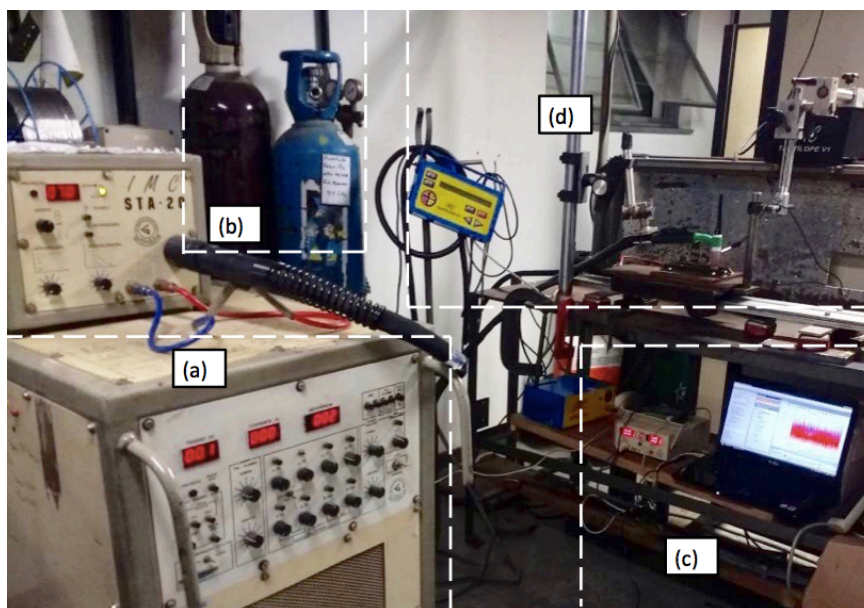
Montagem do equipamento para soldagem. a) Fonte universal b) Cilindro de gás (Ar) c) Sistema de aquisição de dados d) Tocha acoplada a tartaruga.
